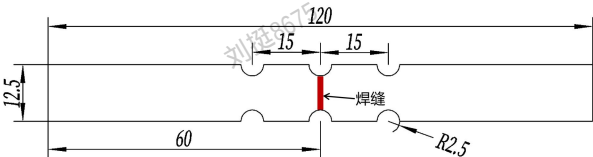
焊缝氢脆拉伸评价试样示意图及尺寸（mm）
